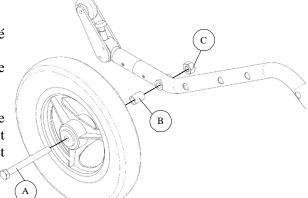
Installation de la roue arrière de 12 po (31 cm)
